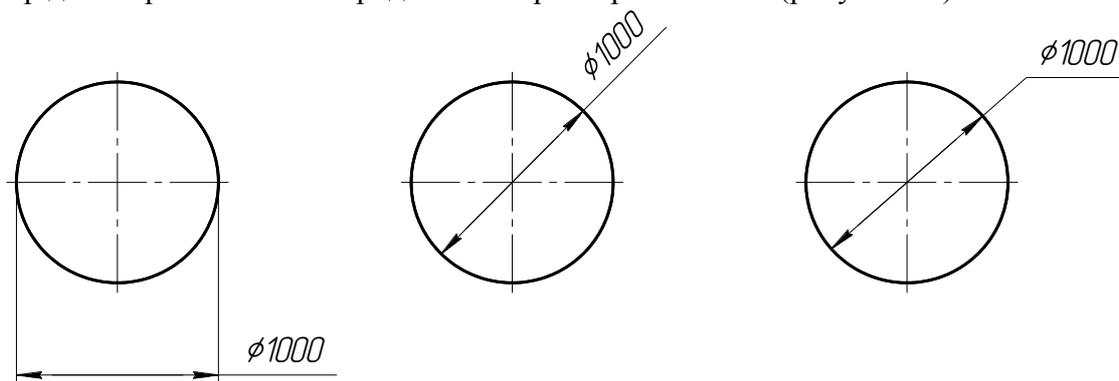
Нанесение размеров диаметров, когда нет места для размерного числа
